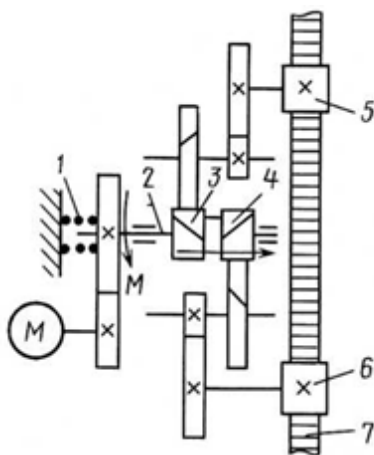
Кинематическая схема привода с зубчато-реечной передачей
